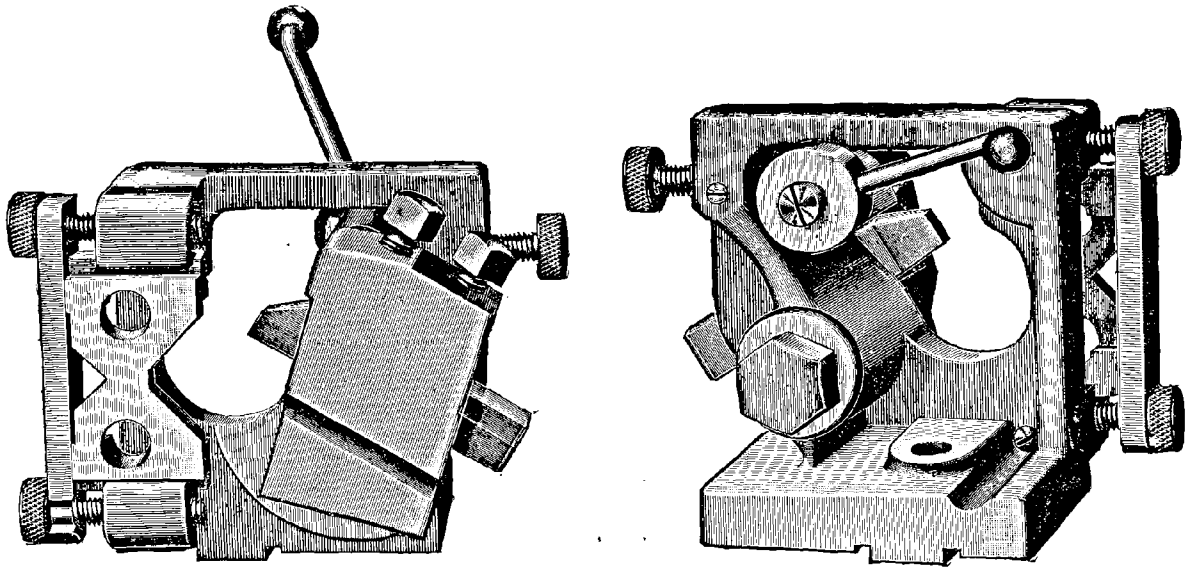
et 509. — Porte-outil de tournage, vue devant et derrière.
